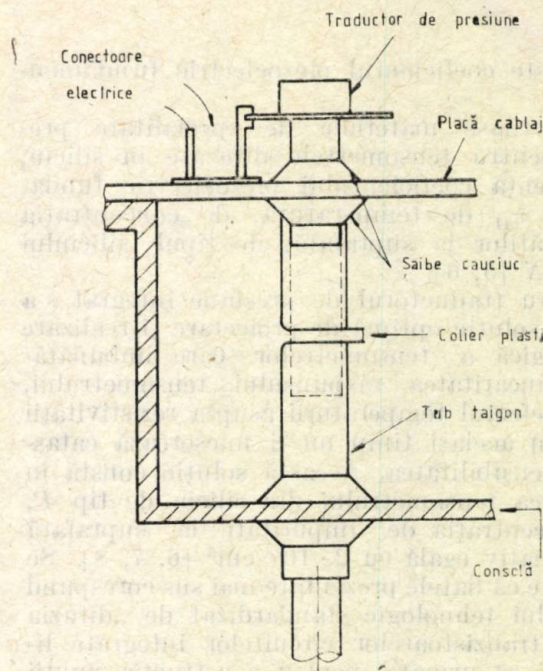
Montarea în panoul pentru probe a traductorului de presiune.
